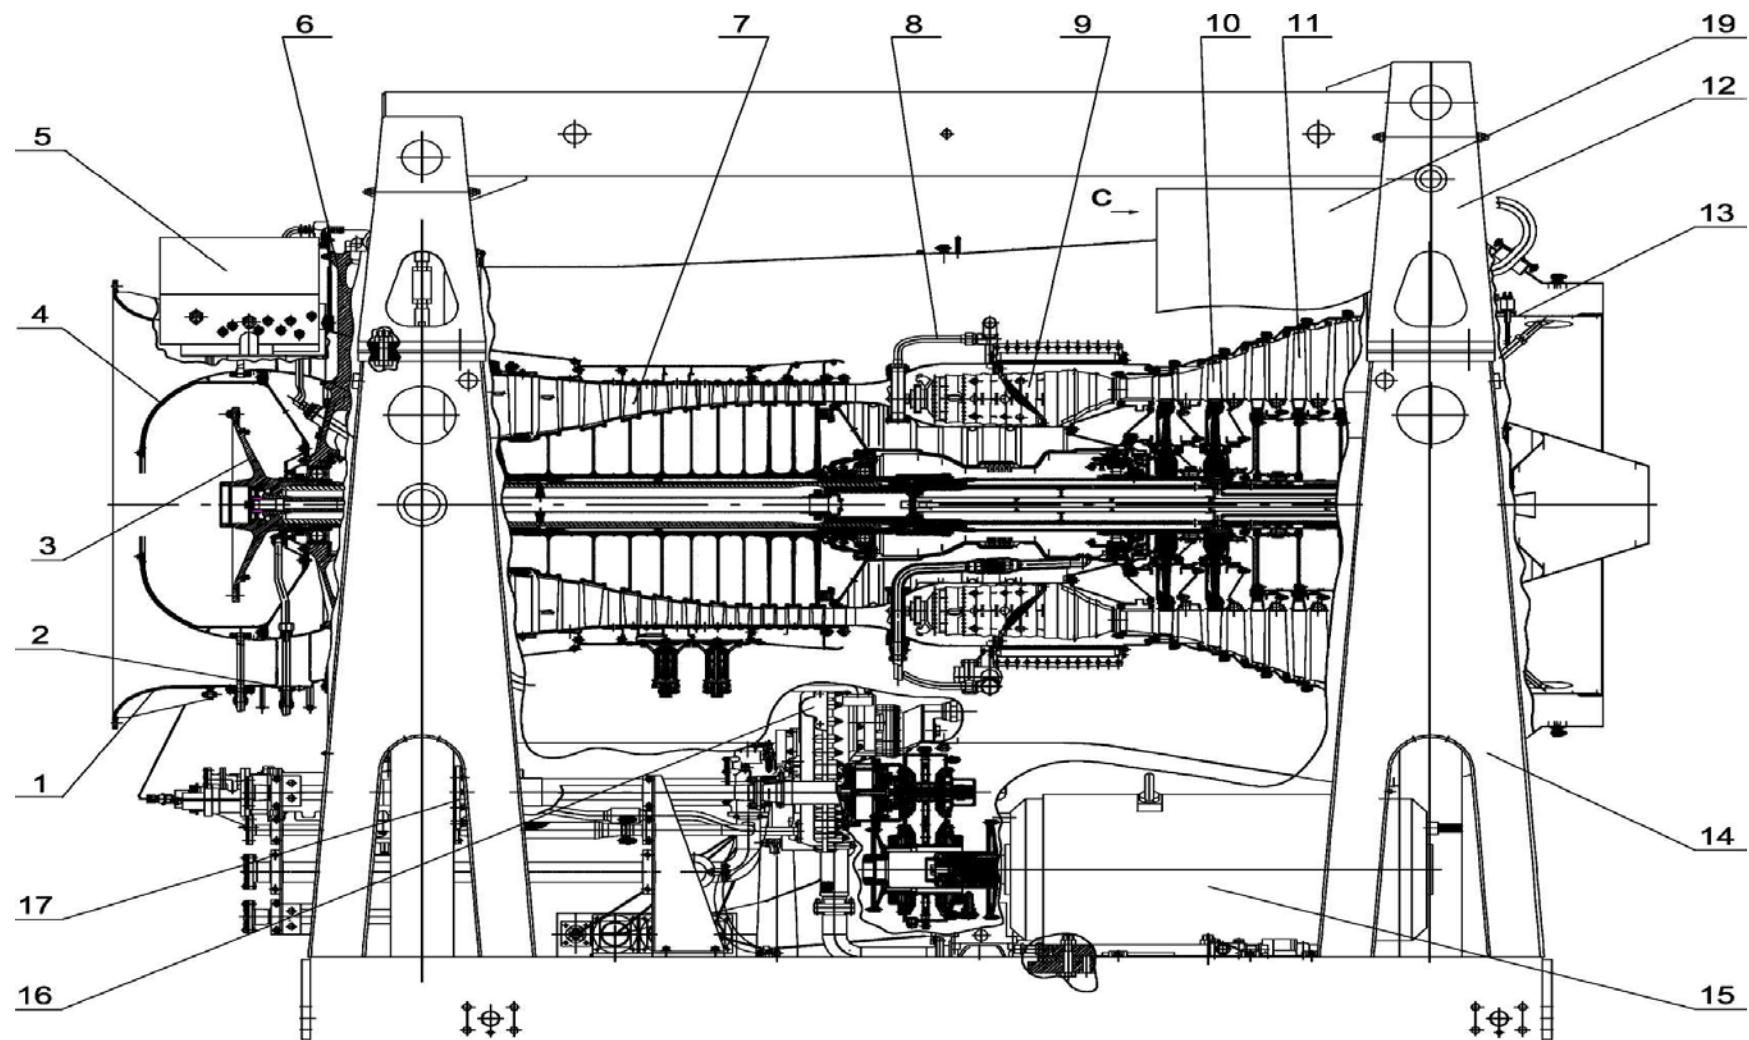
Состав двигателя на раме: 1 – лемниската, 2 – корпус входной, 3 – трансмиссия, 4 – обтекатель с обечайкой кока, 5 – агрегат исполнительных клапанов, 6 – разделительный корпус, 7 – компрессор, 8 – топливный коллектор, 9 –
